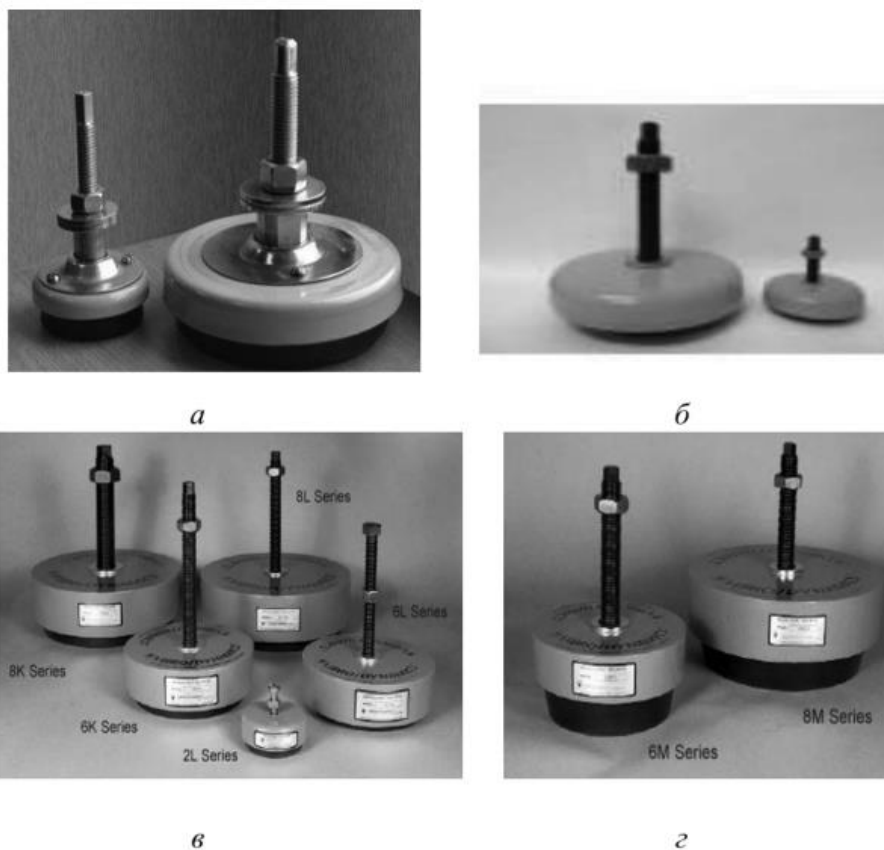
Віброізолюючі опори верстатів: а,б – з гумово-металевою підшоною; в – з підвищеною піддатливістю, пневматичні; г – для координатно-вимірювального обладнання та шліфувальних верстатів
